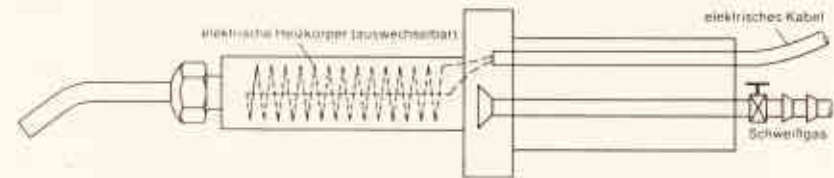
Heißfächelgasschweißen
